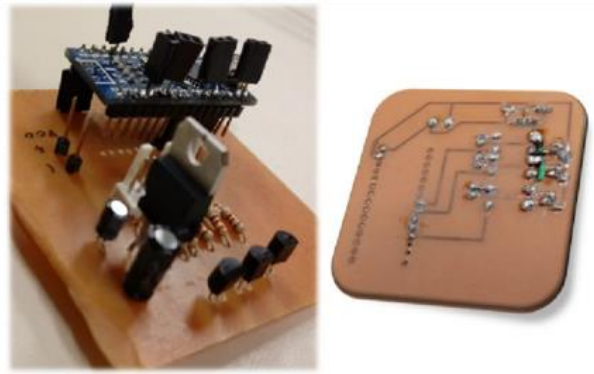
PCB Confeccionada através do método de termotransferência com os componentes soldados.
